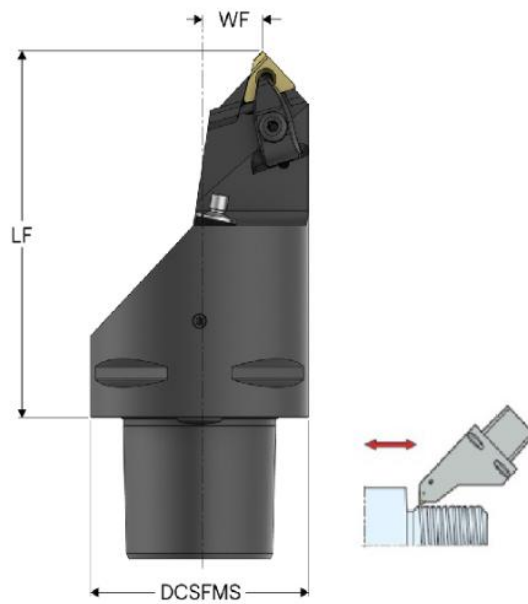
Державка C6-CER/L-18100-16HD [2. с.96]
